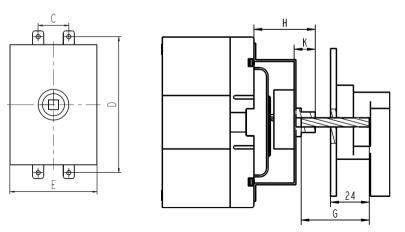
Габаритные и установочные размеры ручки на дверь шкафа РП-330Е, мм
